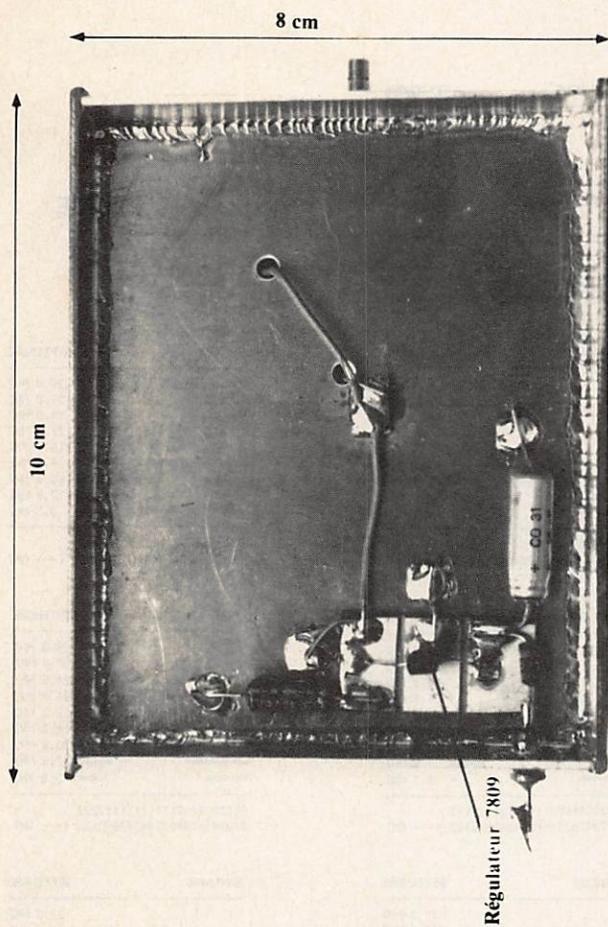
Vue de l'oscillateur local côté régulateur 7809.
